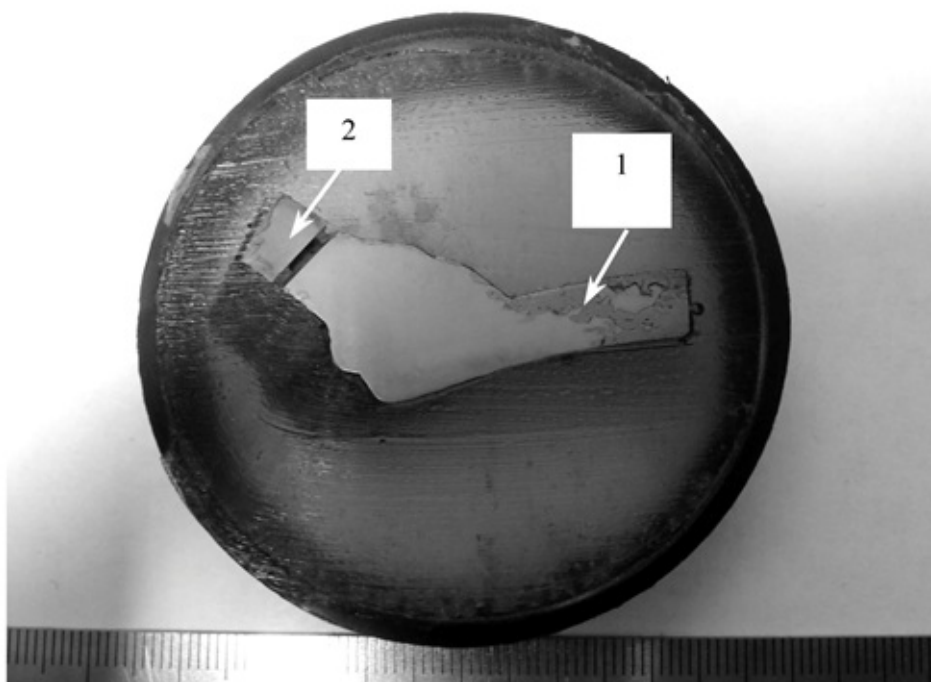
Внешний вид темплета №1 сварного шва узла врезки:
